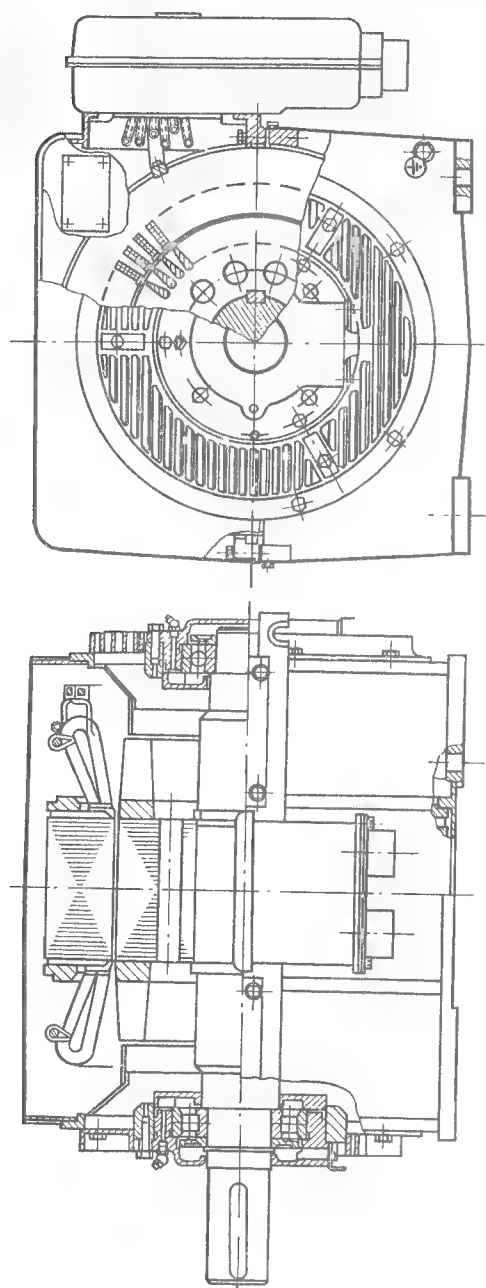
Общий вид защищенного двигателя (IP23) с высотой оси вращения 315 мм со сварной станиной
